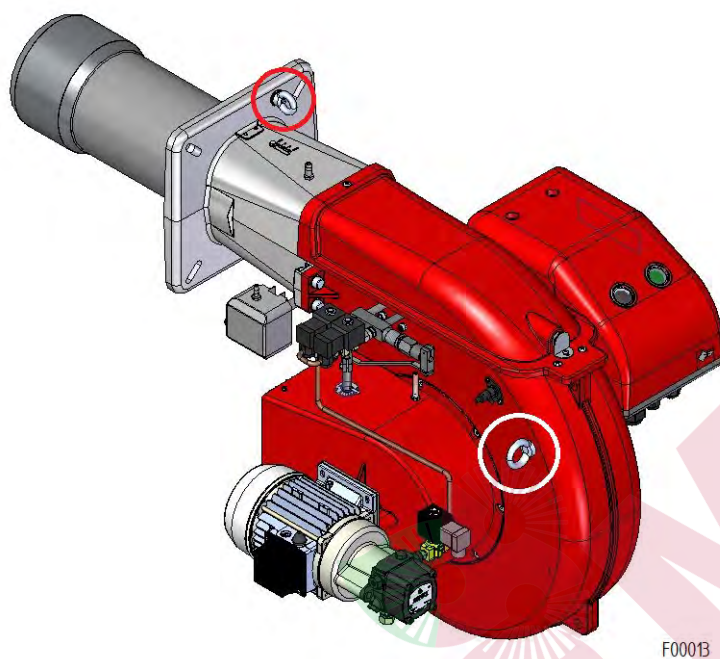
Транспортировочные рым-болты FGP 75/M - 100/M EVO
